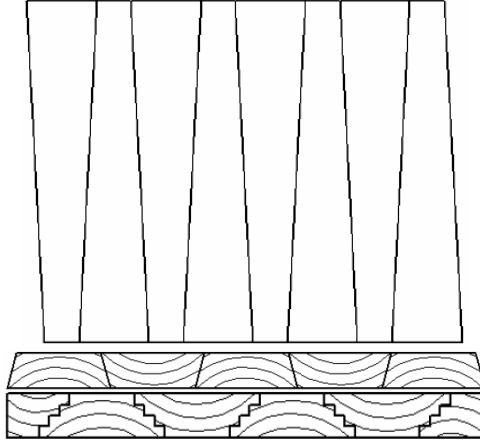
Схема расположения деталей при изготовлении клееного щита из заготовок трапециевидной формы.
